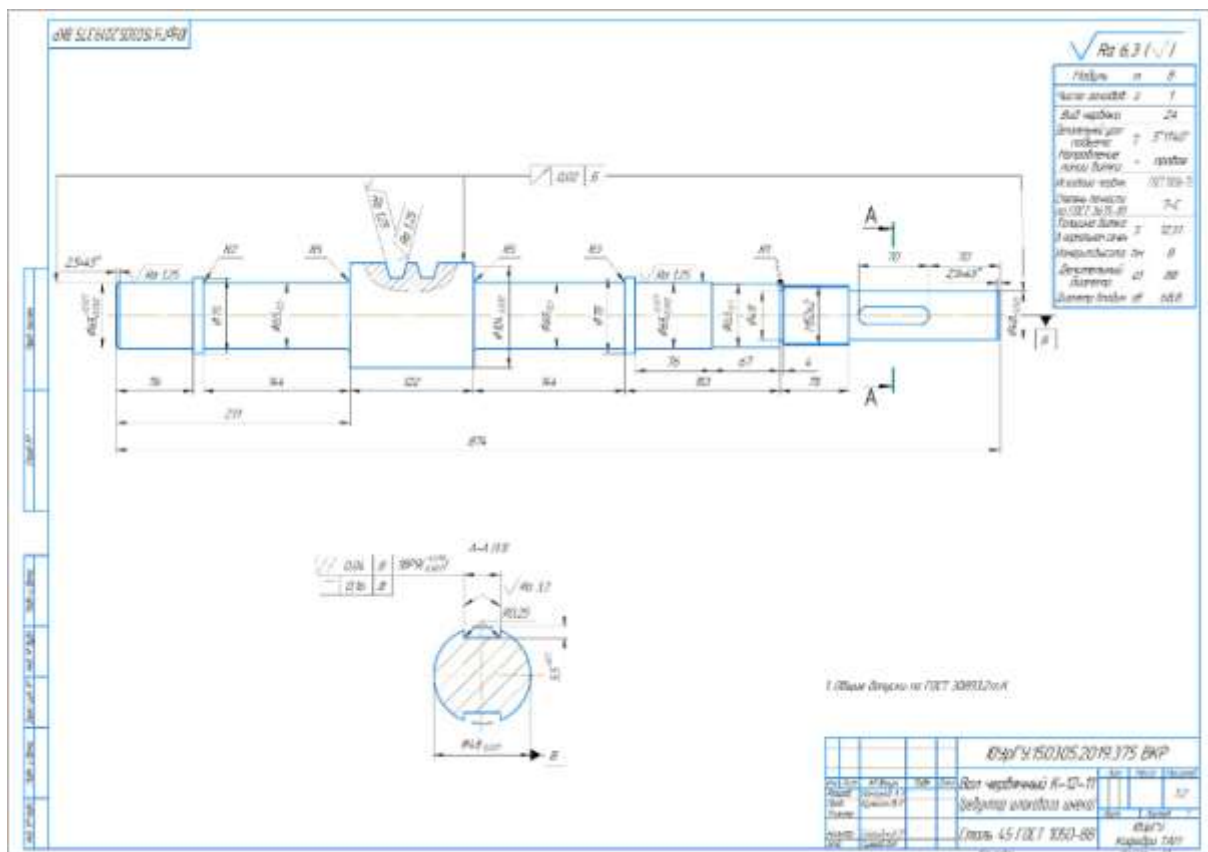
Конструкторский чертеж детали «Вал К-12-11»
